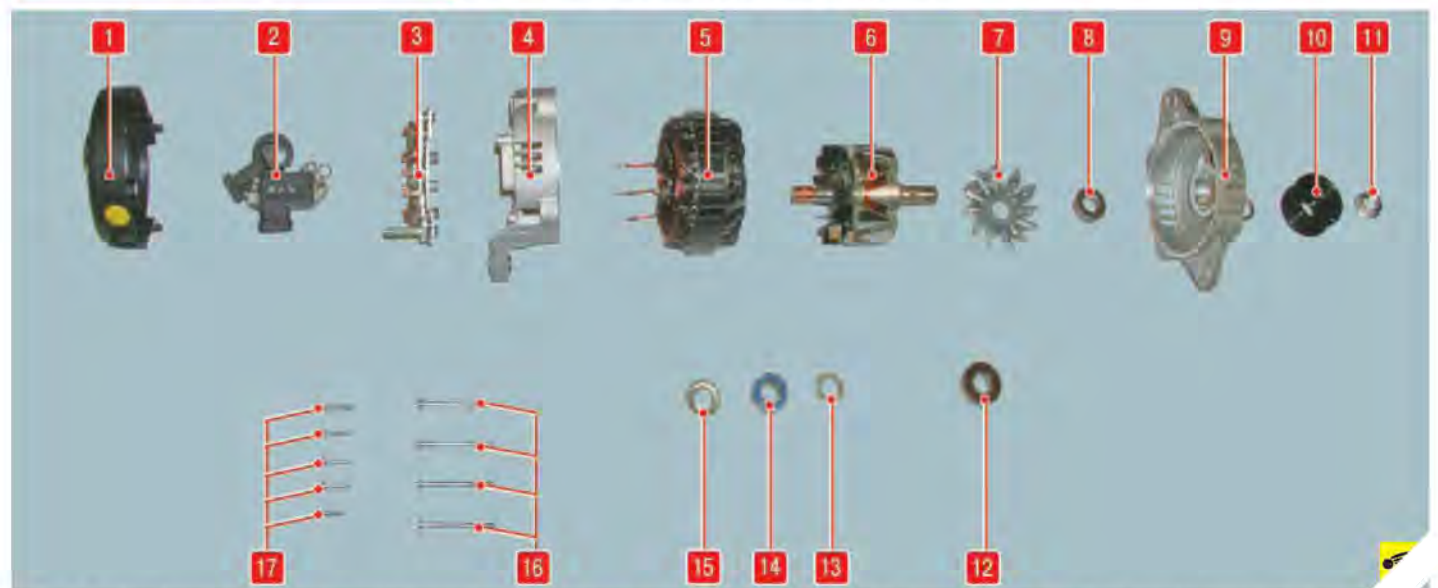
Детали генератора: 1 – кожух; 2 – регулятор напряжения, объединенный со щеточным узлом; 3 – выпрямительный блок; 4 – крышка со стороны контактных колец; 5 – статор; 6 – ротор; 7 – крыльчатка вентилятора; 8 – дистанционная втулка; 9 – крышка со стороны привода; 10 – шкив; 11 – гайка крепления шкива; 12 – передний подшипник вала ротора; 13 – защитная шайба заднего подшипника ротора со стороны обмотки; 14 – задний подшипник ротора; 15 – защитная шайба заднего подшипника ротора со стороны контактных колец; 16 – стяжные болты; 17 – болты крепления регулятора напряжения и выпрямительного блока
